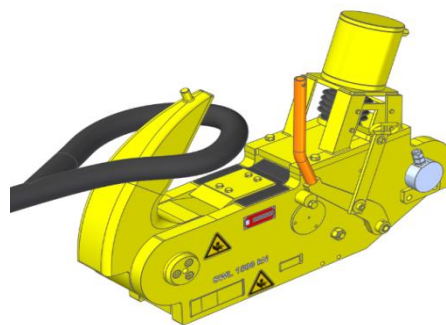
Visão geral da unha do gancho (Adaptado de Mampaey, 2019)
